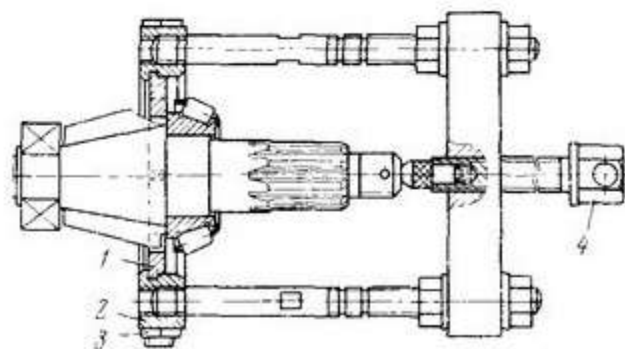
Снятие внутреннего кольца заднего конического подшипника ведущей шестерни
